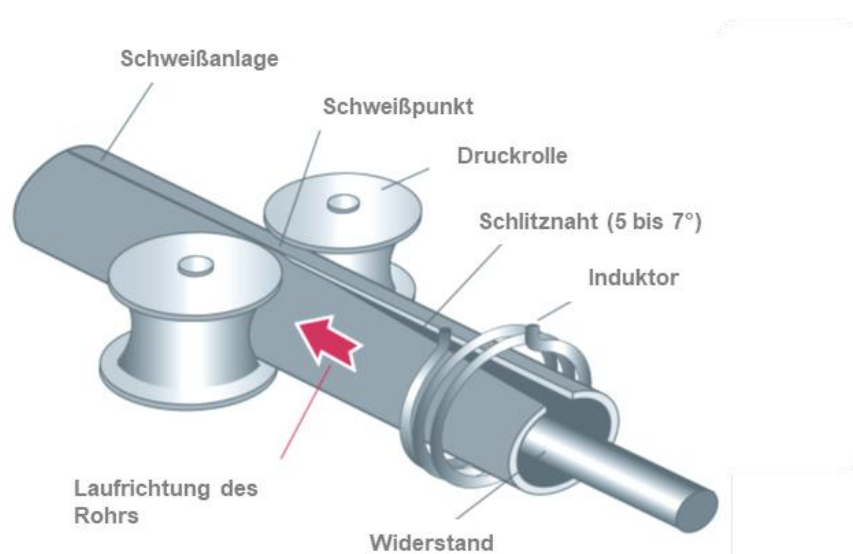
Prinzipskizze-HF-Schweißung [10]
